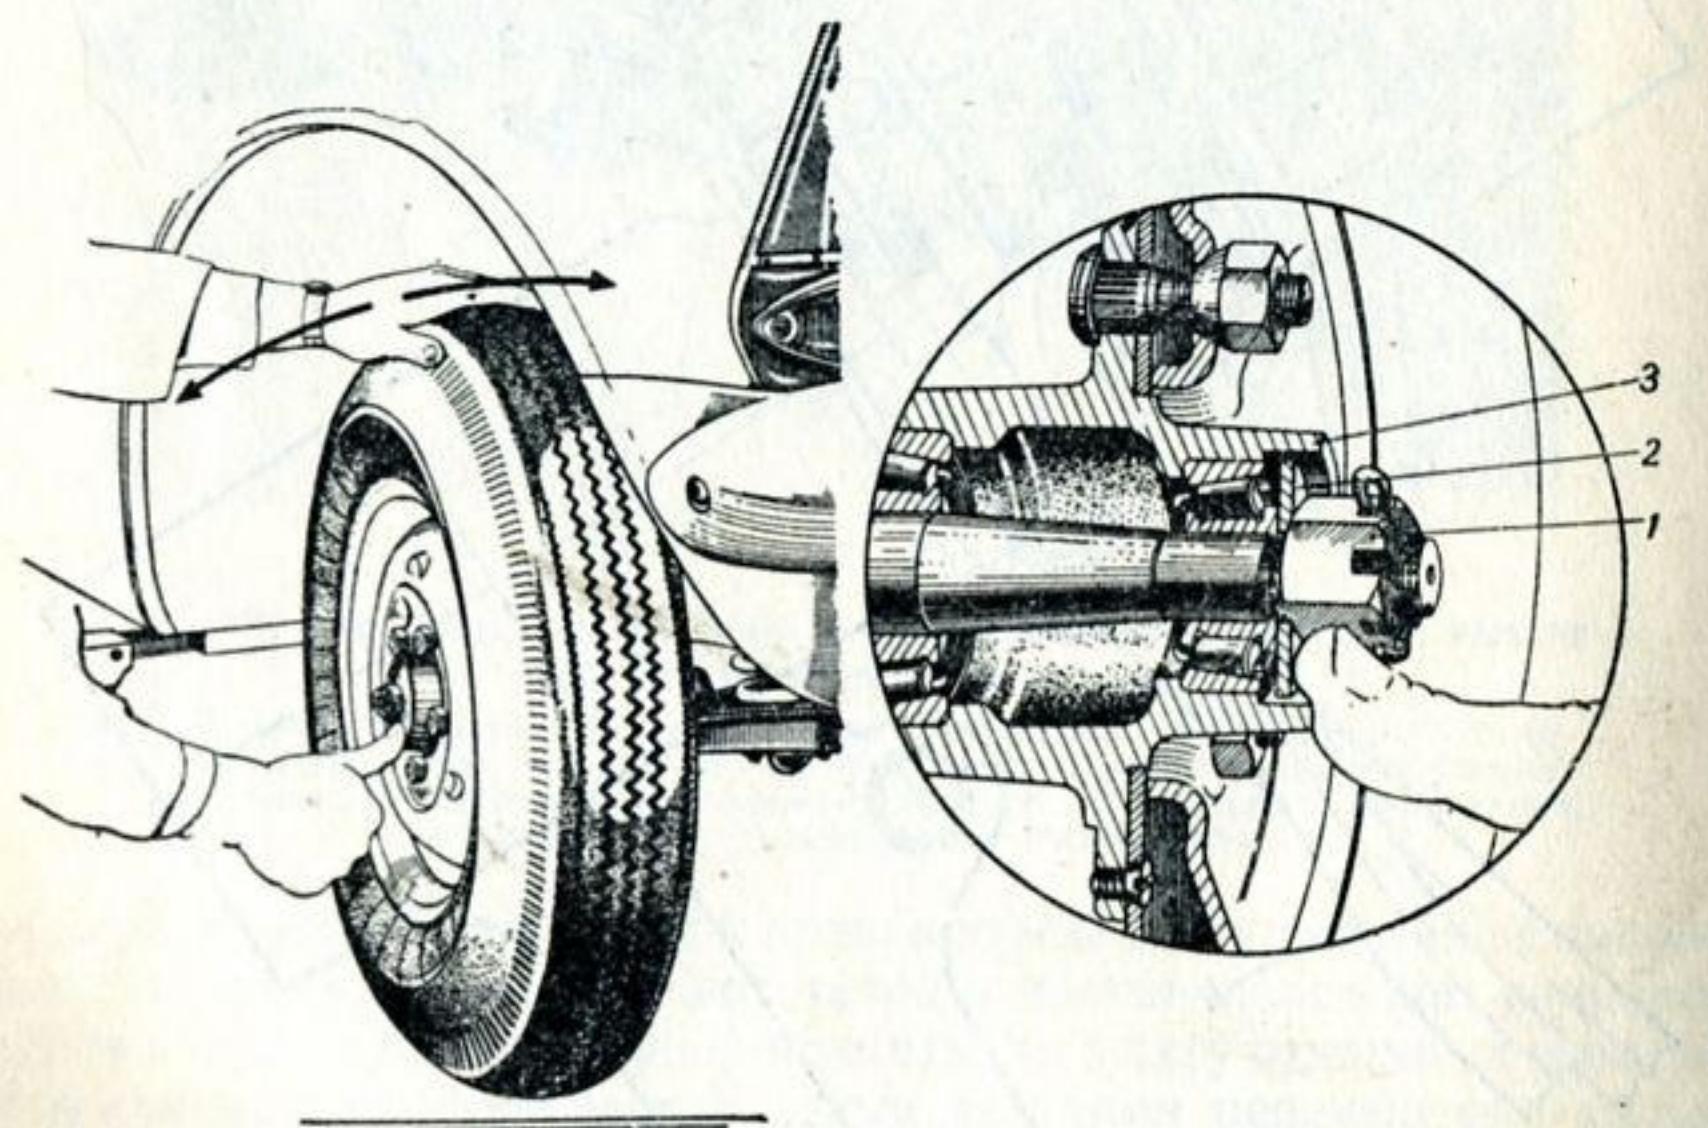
Проверка подтяжки подшипников ступицы переднего колеса:
